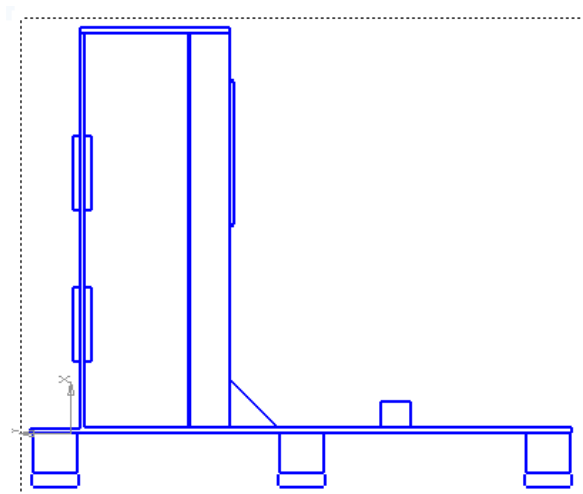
Сварная рама для установки коробки перемены передач
